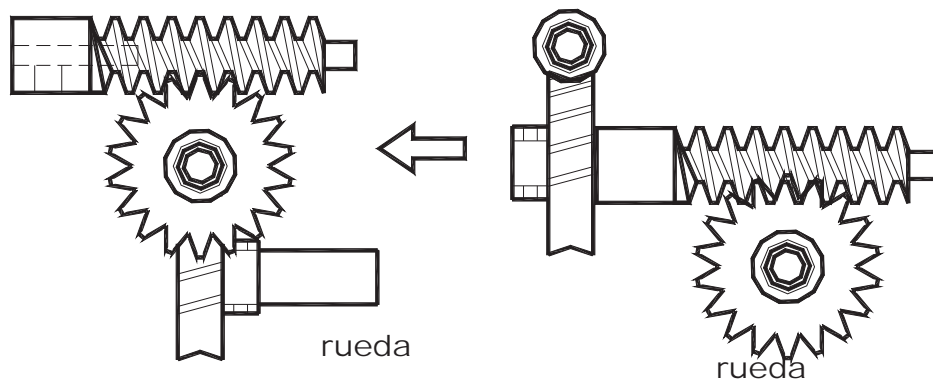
Engranaje de forma de diente gusano (sinfin) y ejes oblicuos (perpendiculares).
